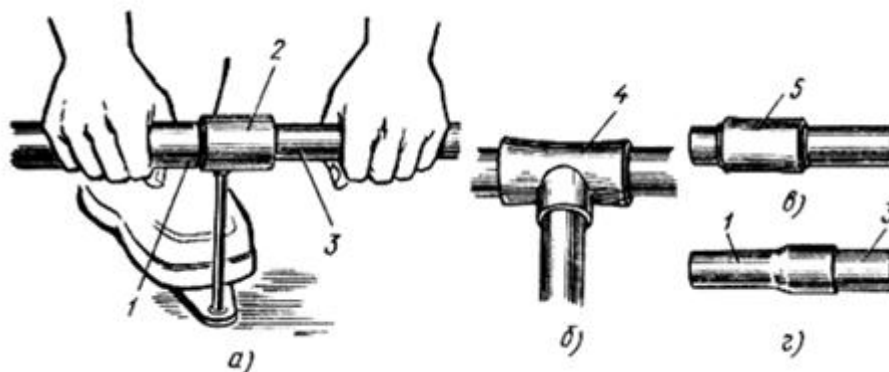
Контактная раструбная сварка (а) в литой тройник (б), муфту (в), раструб (г):
